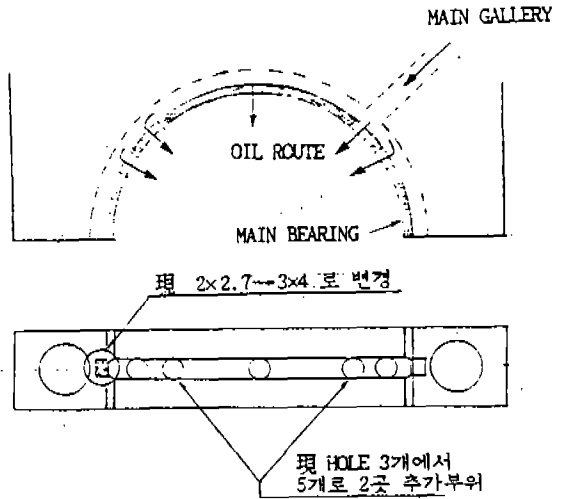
Main Bearing Groove의 Oil Route 변경시 Pin 온도
